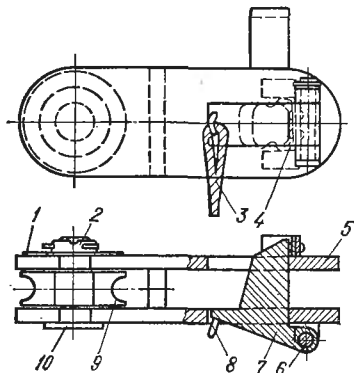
Приспособление для строповки к полуавтоматическому стропоу конструкции треста Востокметаллургмонтаж:
